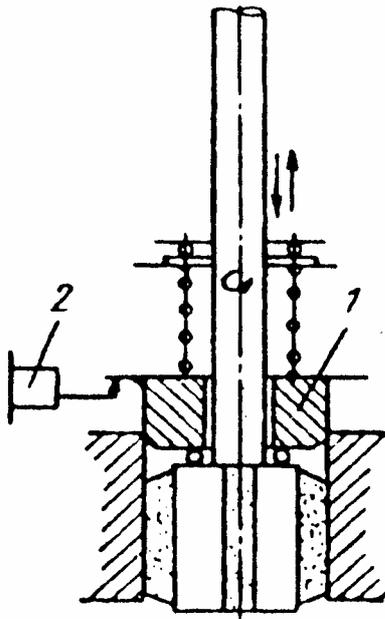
Схема измерительного устройства хонинговального станка: 1 – жесткий калибр; 2 – электроконтактный преобразователь
